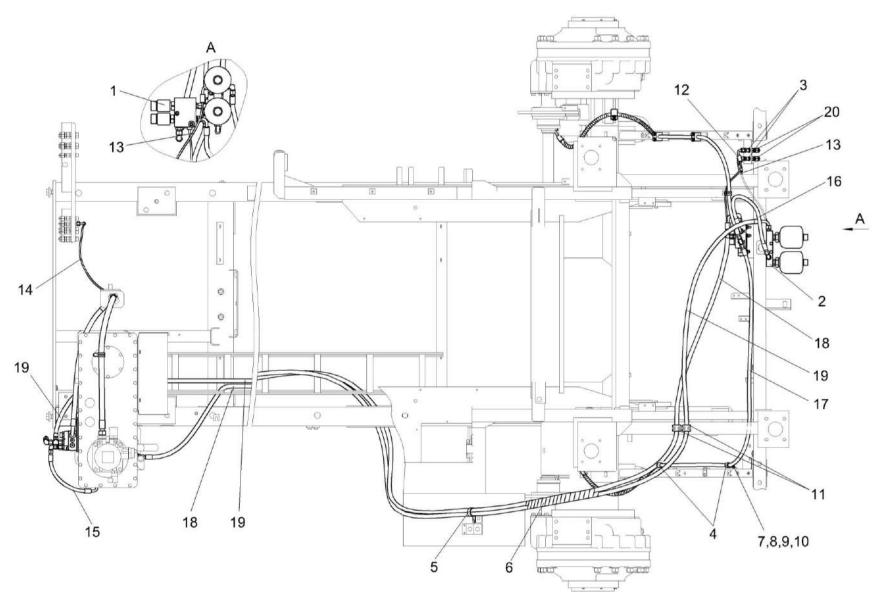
Гидросистема привода стояночного тормоза КВК-2-0606000 (вид сверху) *542
